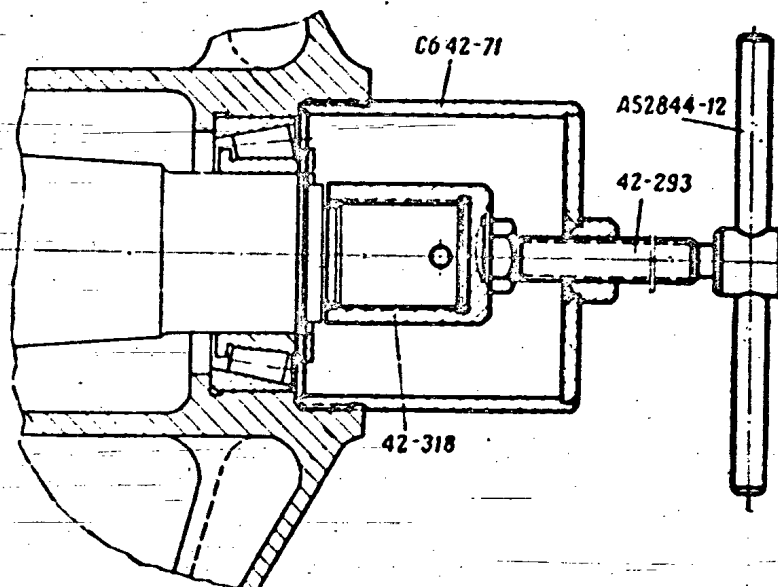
Прибор для снятия колес лафета (*C642-70*):
